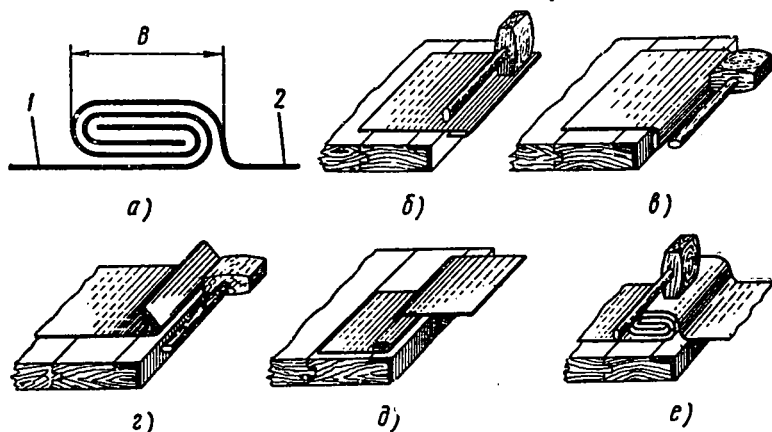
Изготовление двойного лежащего фальца ручным способом:
